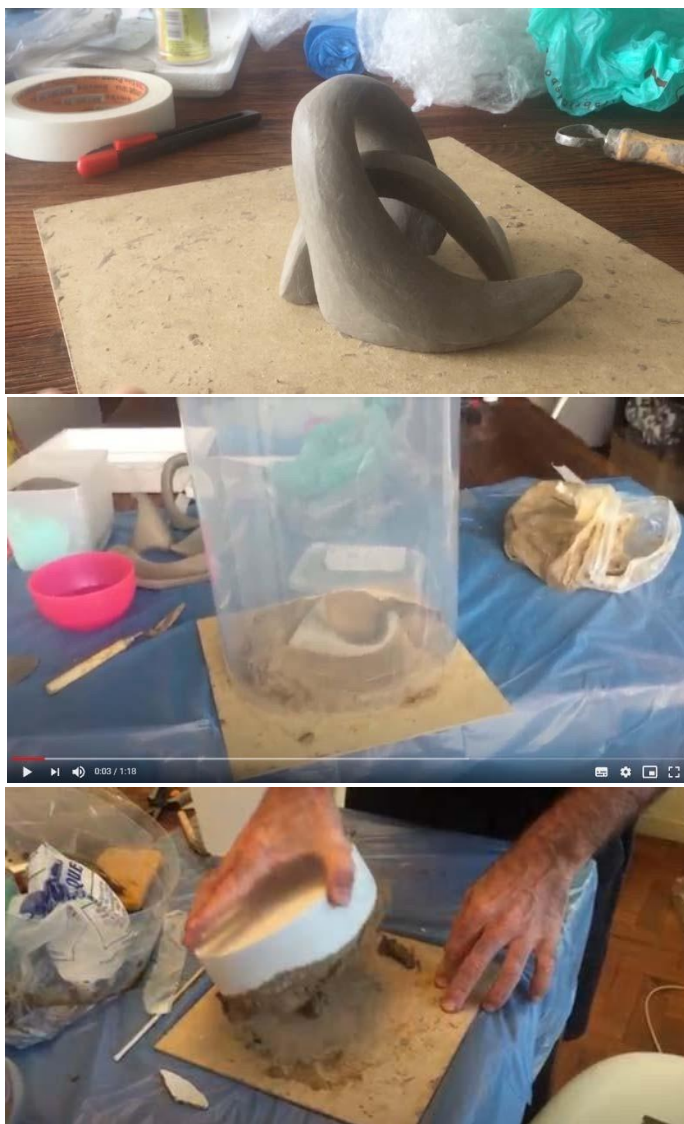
Professor em demonstração para alunos, explicando como deve ser realizado o molde de uma peça em gesso.
